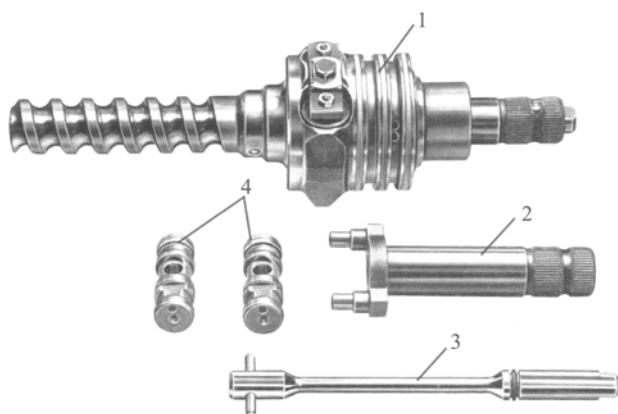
Bauteile eines Drehkolbenventils für eine Kugelumlauflenkung [3.3]. 1 Ventilkörper, 2 Lenkspindel mit Zapfen, 3 Drehstab, 4 Steuerkolben
